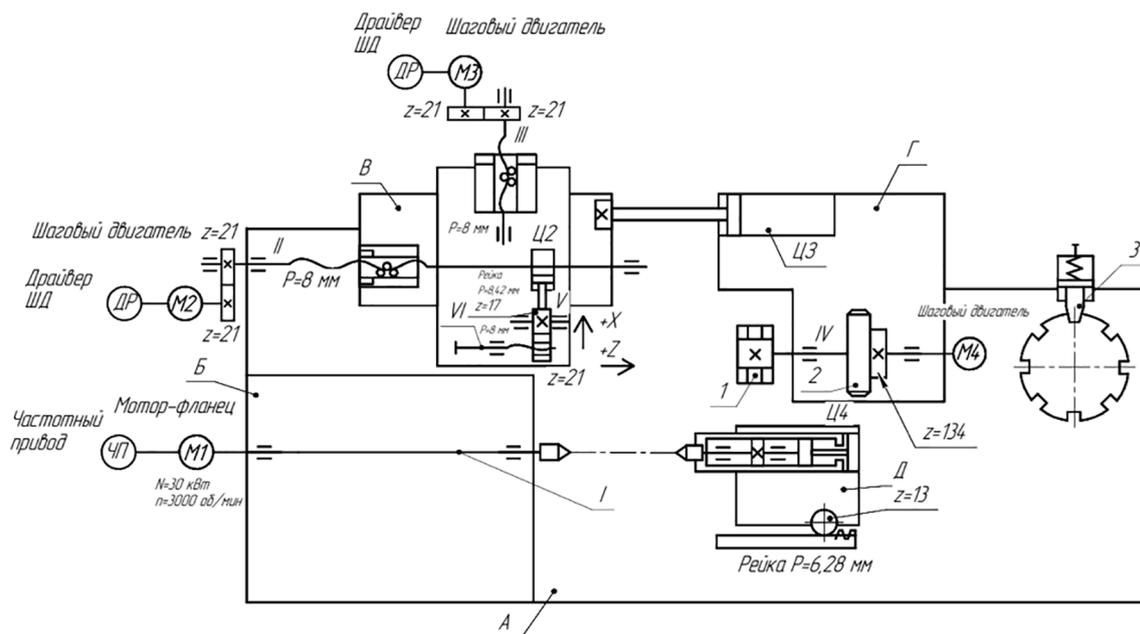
Модернизированная кинематическая схема станка с ЧПУ 1725МФ3
